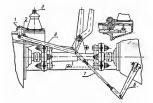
Регулировка механизма блокировки и управления центральной муфтой сцепления тракторов ДТ-54 и ДТ-54А:
